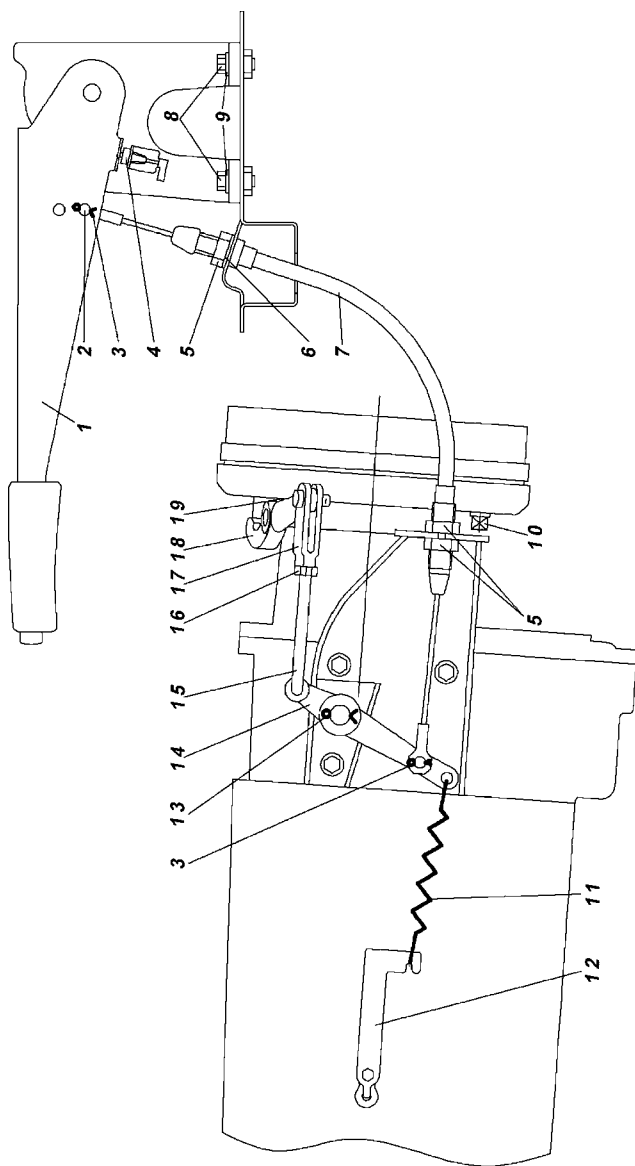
Привод стояночного тормозного механизма для автомобилей с пятиступенчатой коробкой передач:
